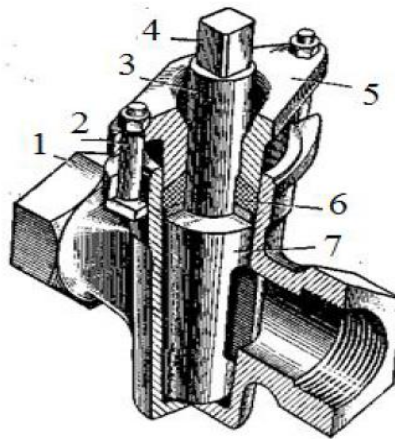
Циліндричні крани: 1 – корпус; 2 – болт; 3 – шток; 4 – головка; 5 – кришка сальника; 6 – сальникове набивання; 7 – конусна пробка
